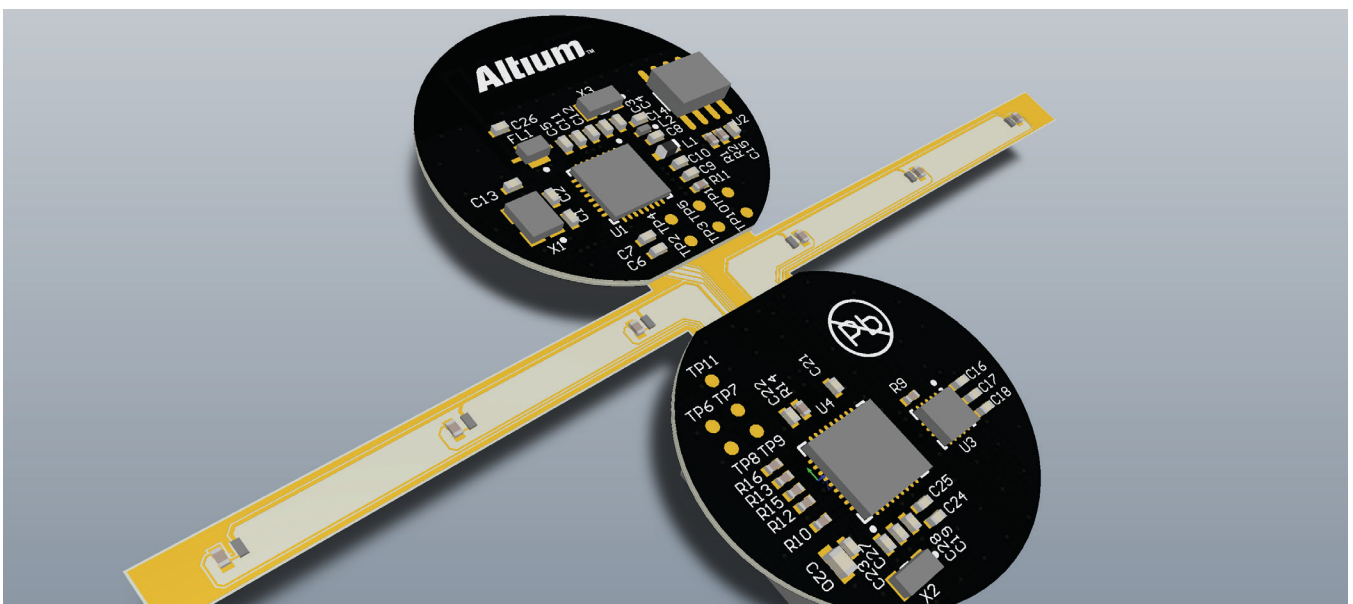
Il software di progettazione PCB che fornisce la modellazione in 3D consente ai progettisti di osservare esattamente come l'assemblaggio PCB si adatta.
